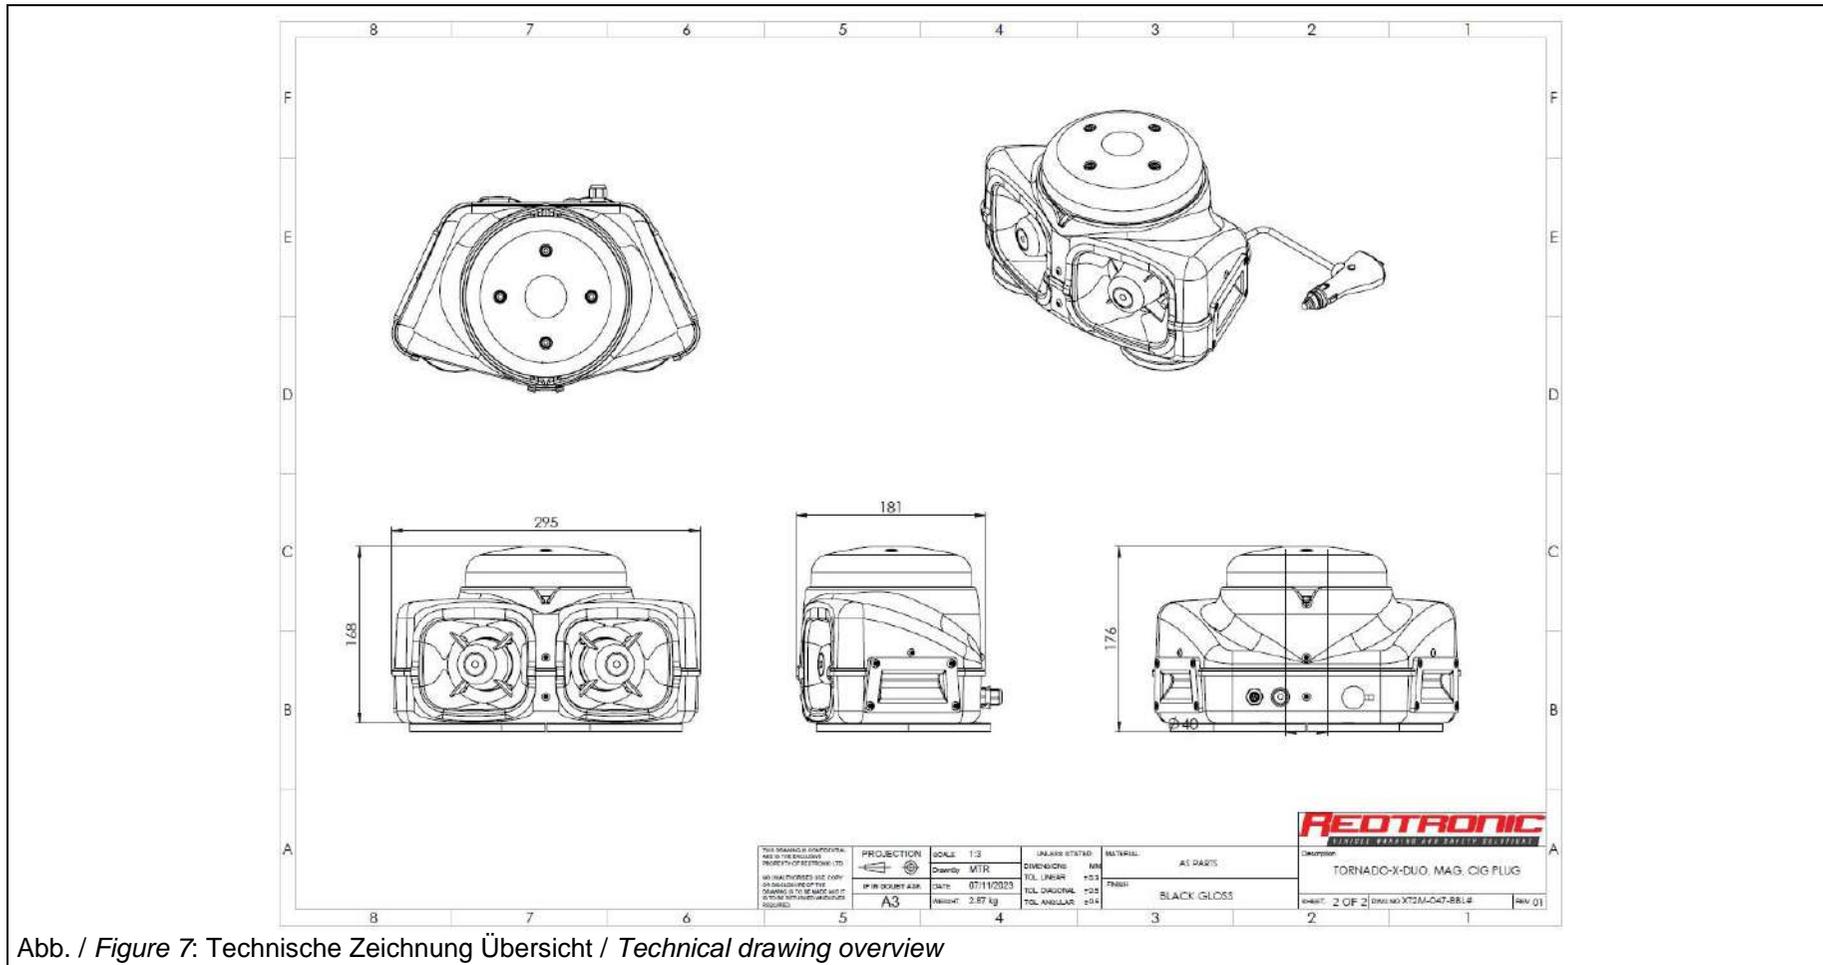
Technische Zeichnung Übersicht / Technical drawing overview
